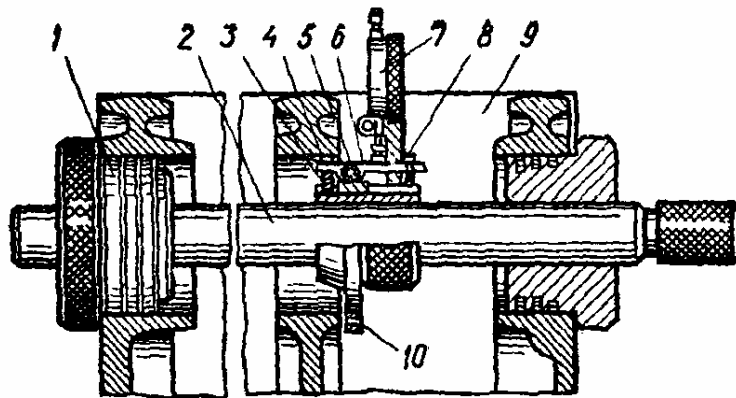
Пристосування для перевірки співвісності отворів у блок-картері під корінні підшипники: 1 - втулка; 2 - оправка; 3 - пружина; 4 - сферичний палець; 5 - вісь; 6 - важіль; 7 - індикатор годинного типу; 8 - регулювальний гвинт; 9 - блок; 10 - упорний штифт
